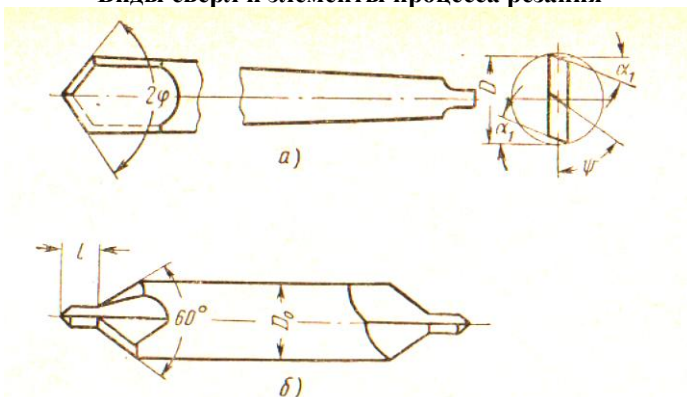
Типы свёрл: а-перовое сверло; б – центровочное сверло
